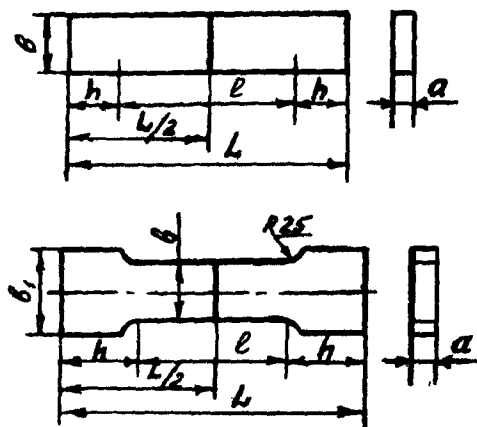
Плоские образцы для испытаний сварных соединений на статическое растяжение
